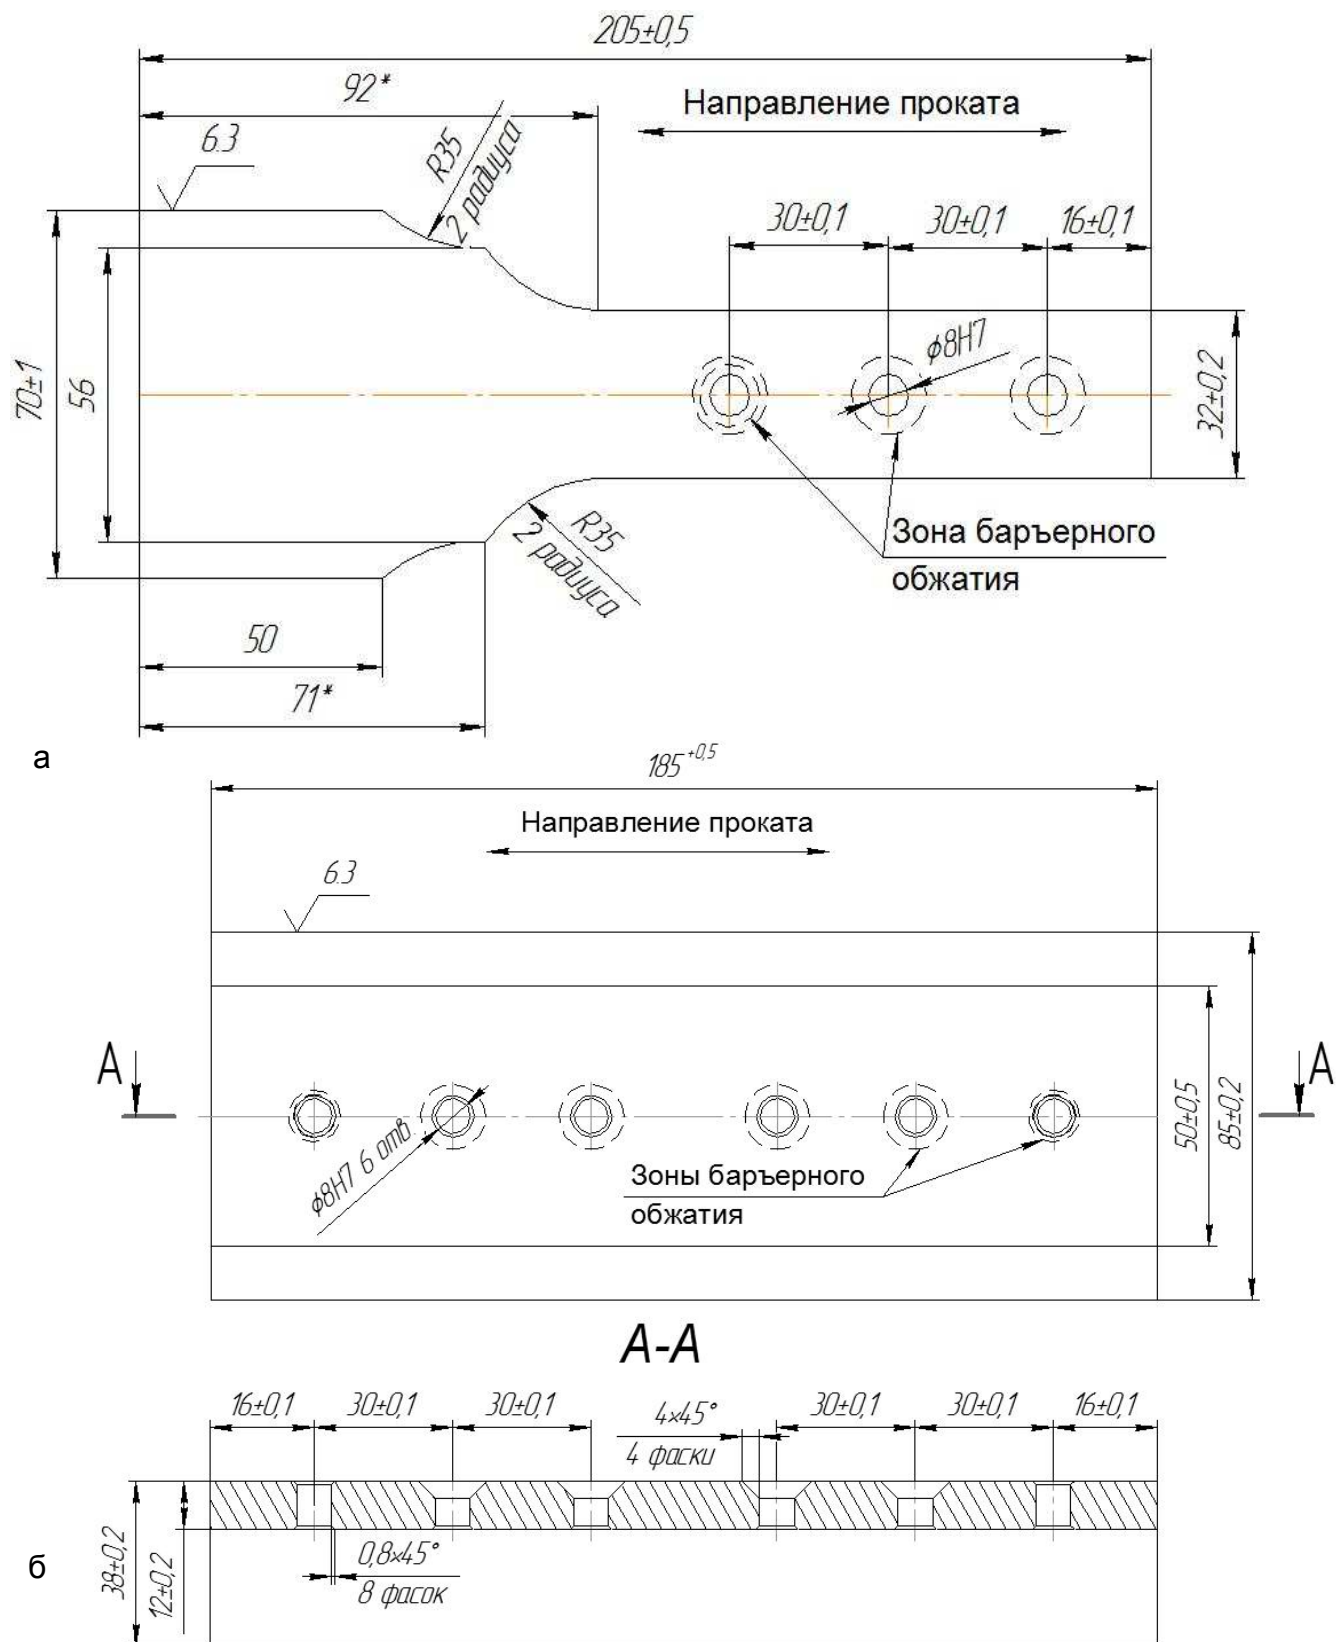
Геометрические размеры деталей для изготовления образцов:
